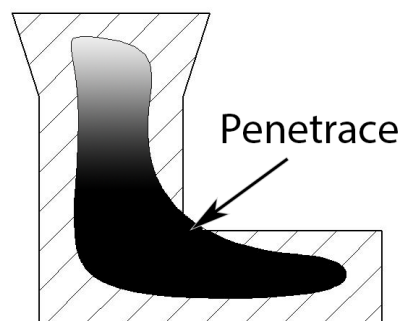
Řez vadou – expanzní penetrace [9]
